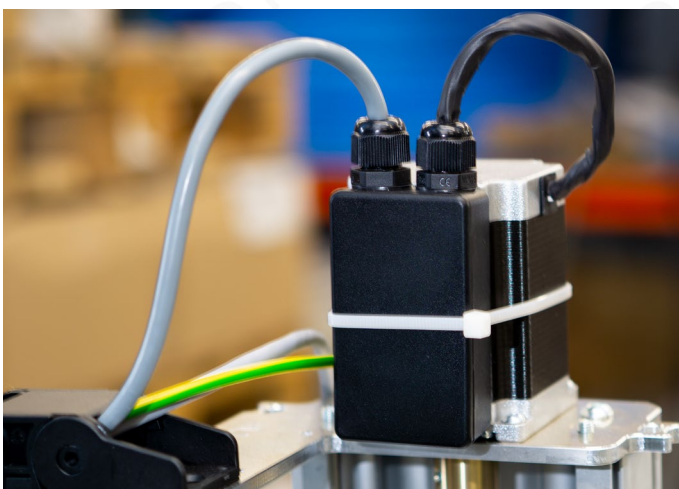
Mit Kabelbinder montierter Klemmenkasten
